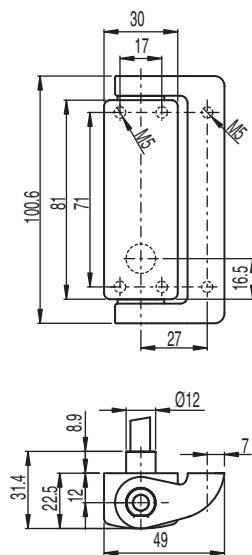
Dimensioni dell'S400-M4-CB2PUR-W in mm
